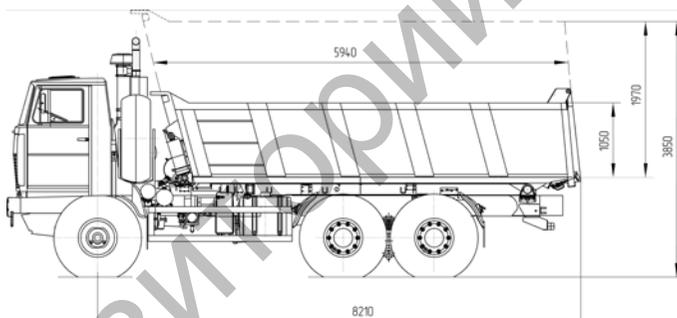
Общий вид автомобиля-самосвала МАЗ-651705
